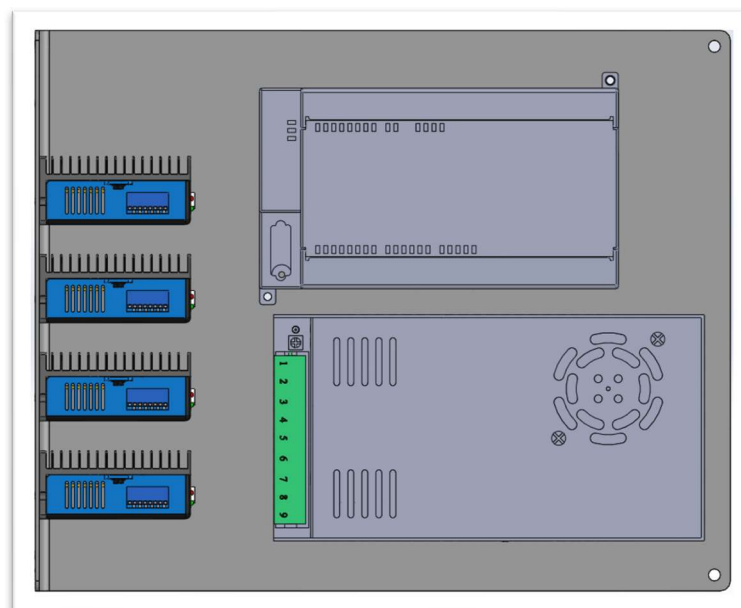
Tablero electrónico de control subgrupo 4 elevadores. Fuente: Elaboración propia
